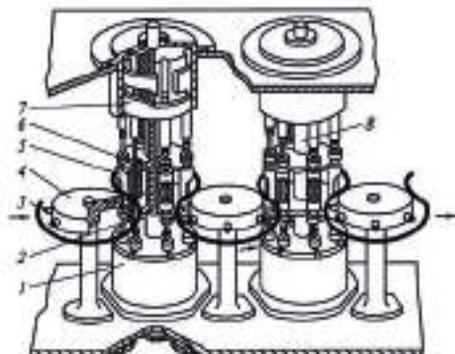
Схема АРЛ: 1 – технологический ротор; 2 – толкатель; 3 – клещи; 4 – транспортный ротор; 5 – суппорт; 6 – патрон; 7 – копир; 8 – колонна
